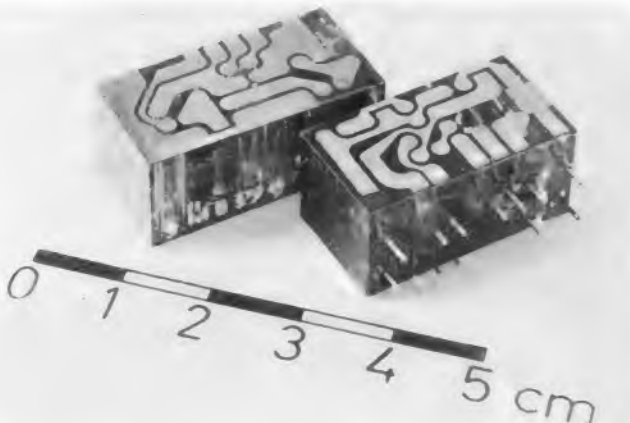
Baugruppen mit Einzelbauelementen (Simiblock-Baugruppen)
